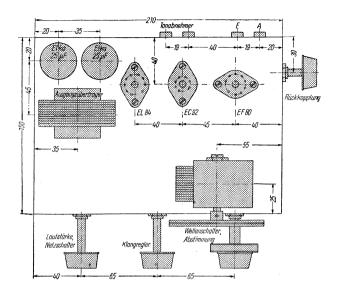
Aufbauplan eines einfachen Einkreis-Empfängers
